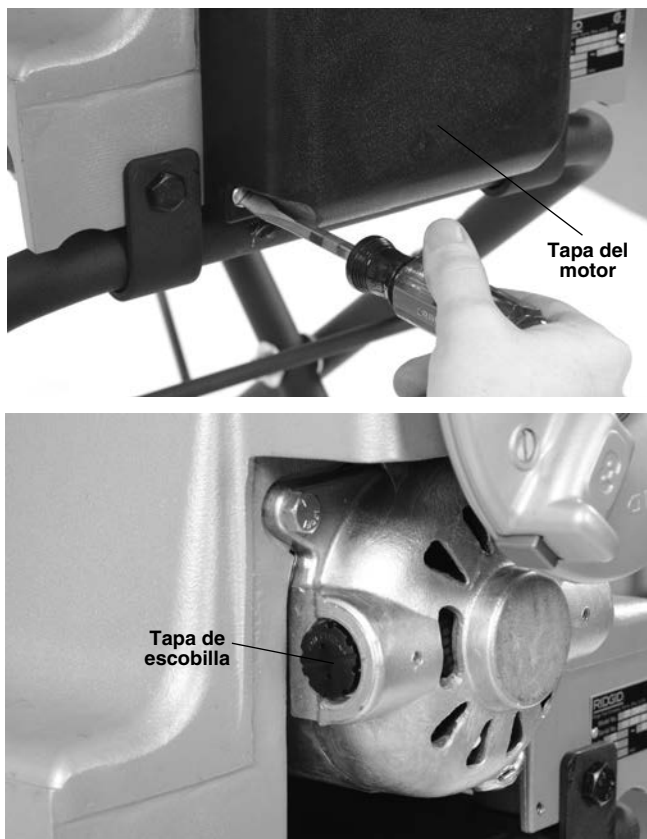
Extracción de la tapa del motor y cambio de las escobillas
